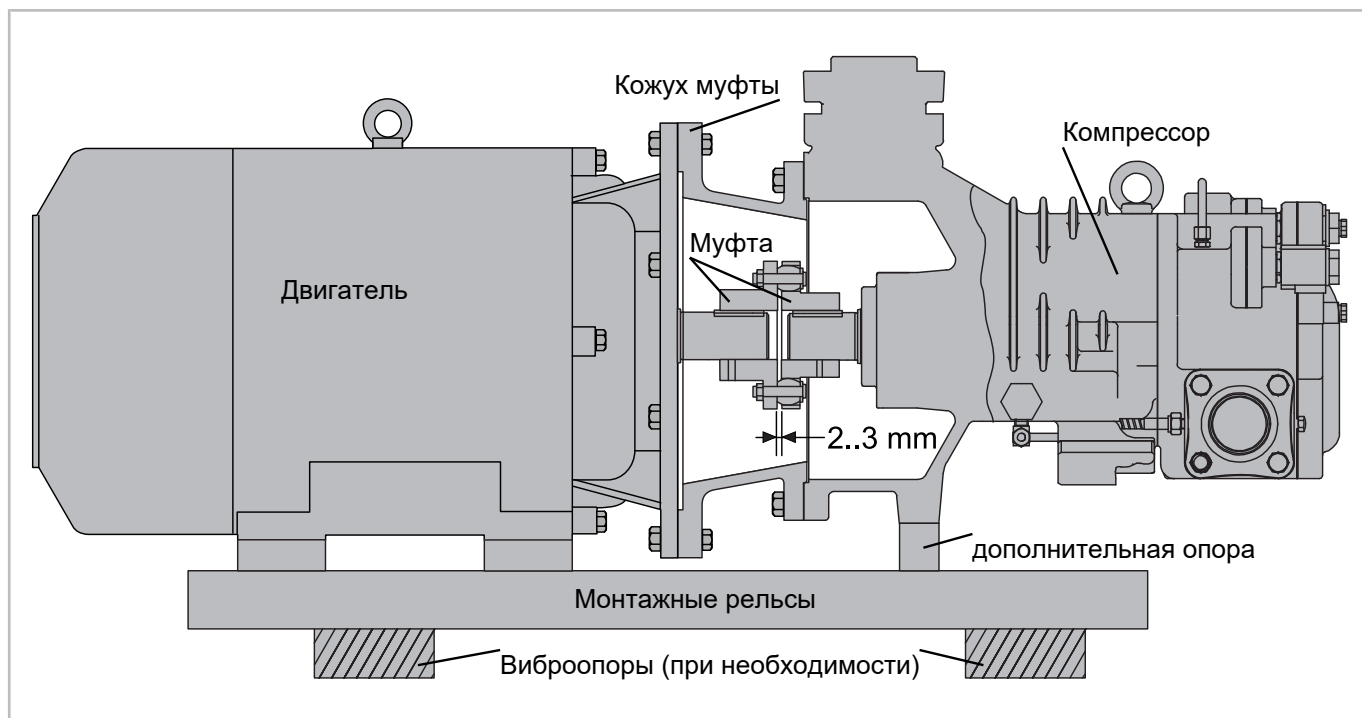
Пример для OS.53 .. 74 компрессоров с двигателем и муфтой
